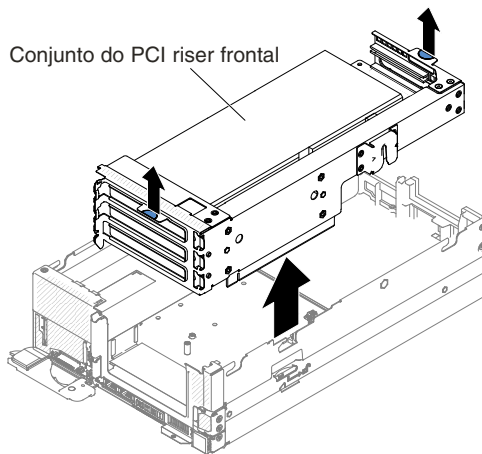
Remoção do conjunto do compartimento da riser PCI frontal
